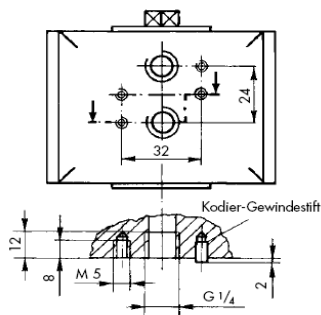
· 1/4" NAMUR Lochbild (Abmessungen in mm)
